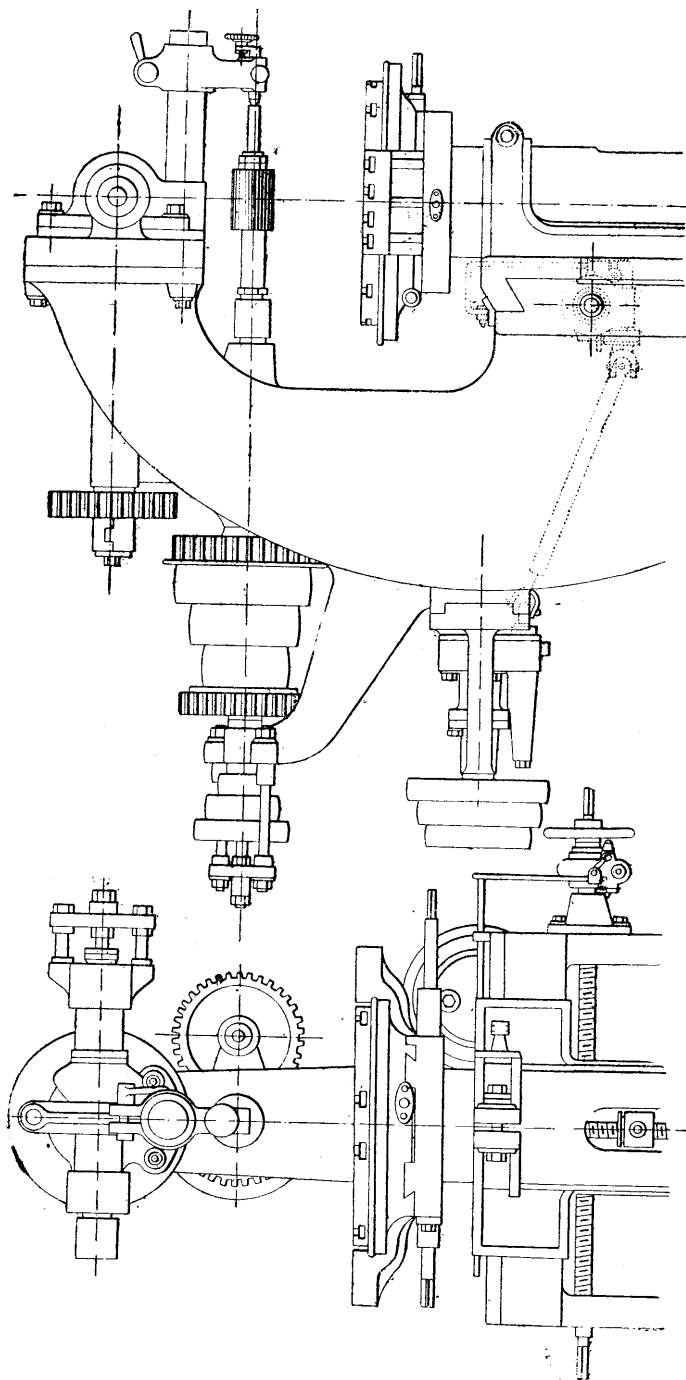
Fraiseuse mixte de M. E. Dubosc, de Turin. — Disposition à fraise horizontale.
